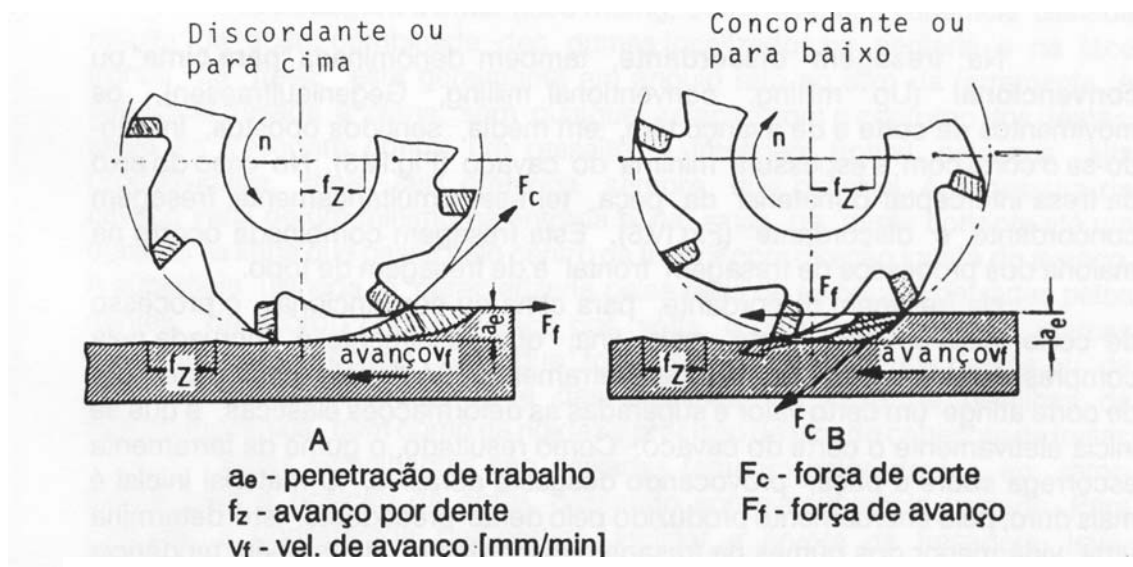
Fresagem periférica A – discordante ou para cima; B – concordante ou para baixo [36]
